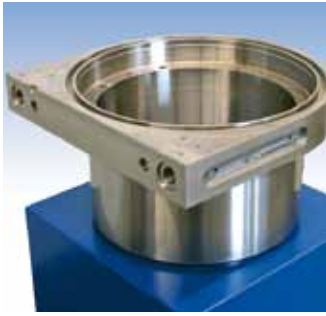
Das Lagergehäuse wurde mit Drehen, Fräsen und Gewindschneiden komplett fertig bearbeitet.
